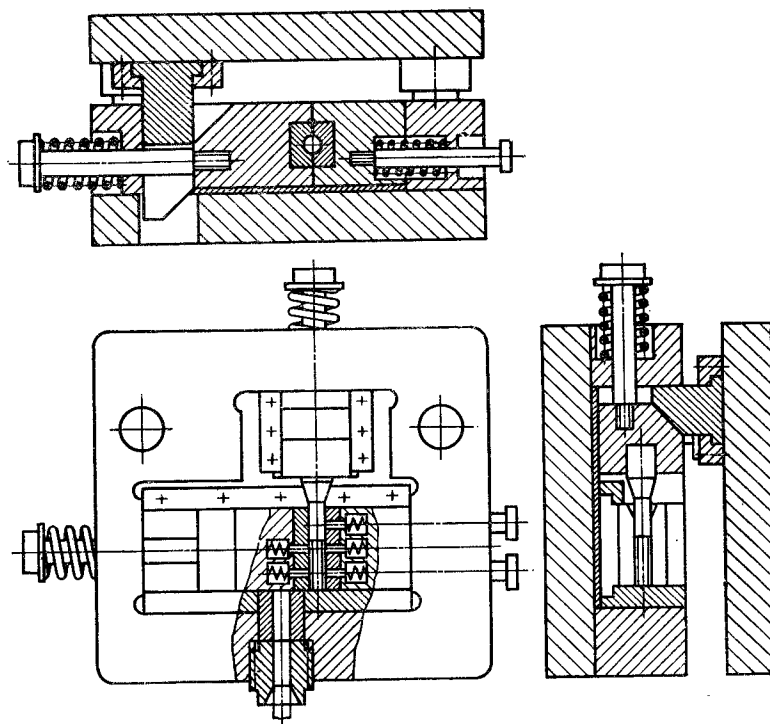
Штамп для неполностью закрытой отрезки и закрытой осадки — калибровки
